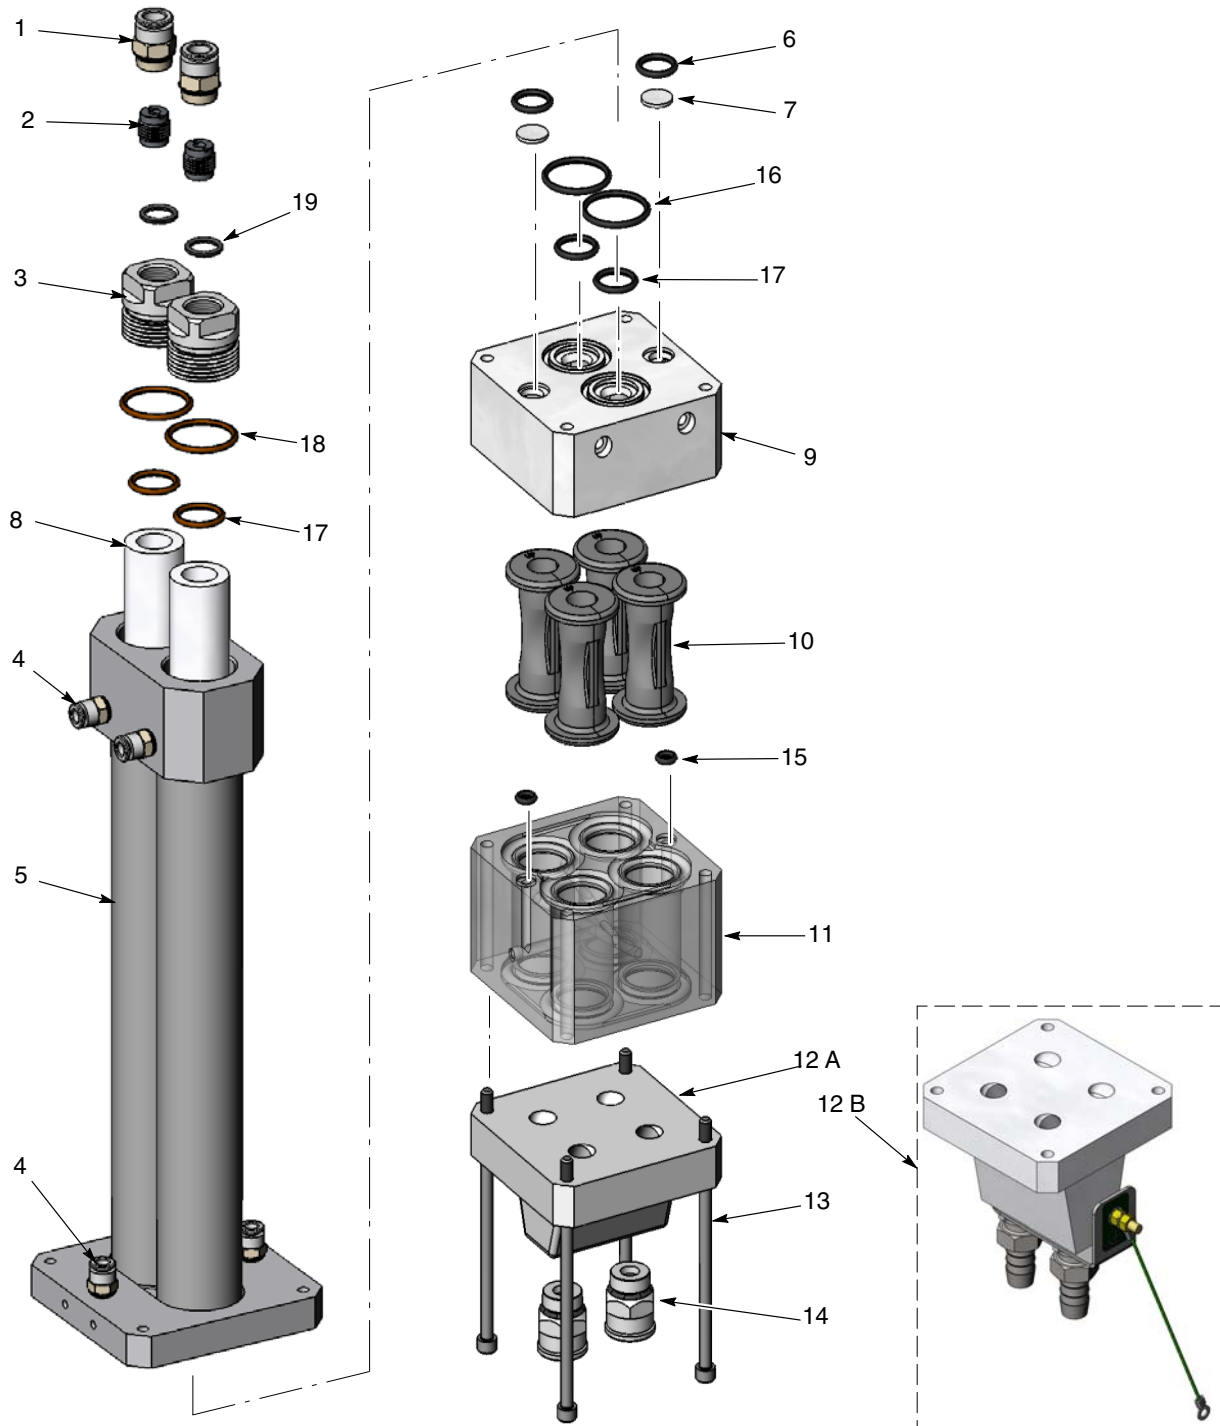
Pumpenbaugruppe ohne Steuerelemente
